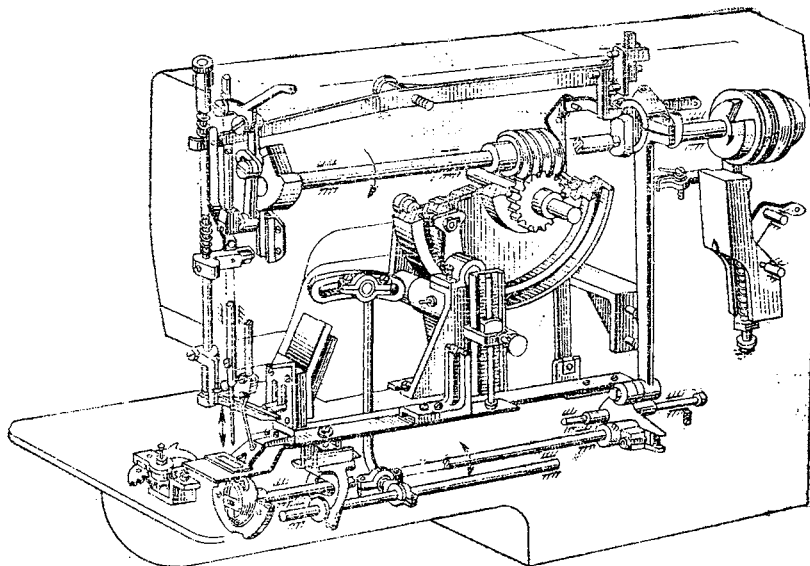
Конструктивная схема машины 220-М кл. и заправка верхней нитки
